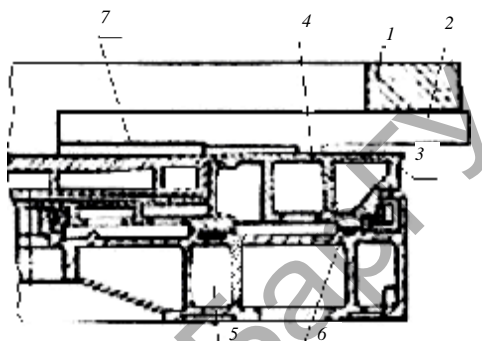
Схема установки крупных заготовок на стол станка
